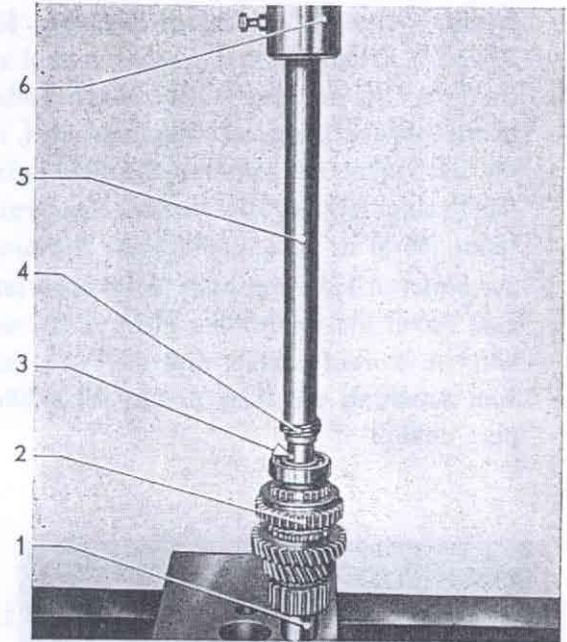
Tachometerschraubenrad auf Hauptwelle von hinten aufpressen
